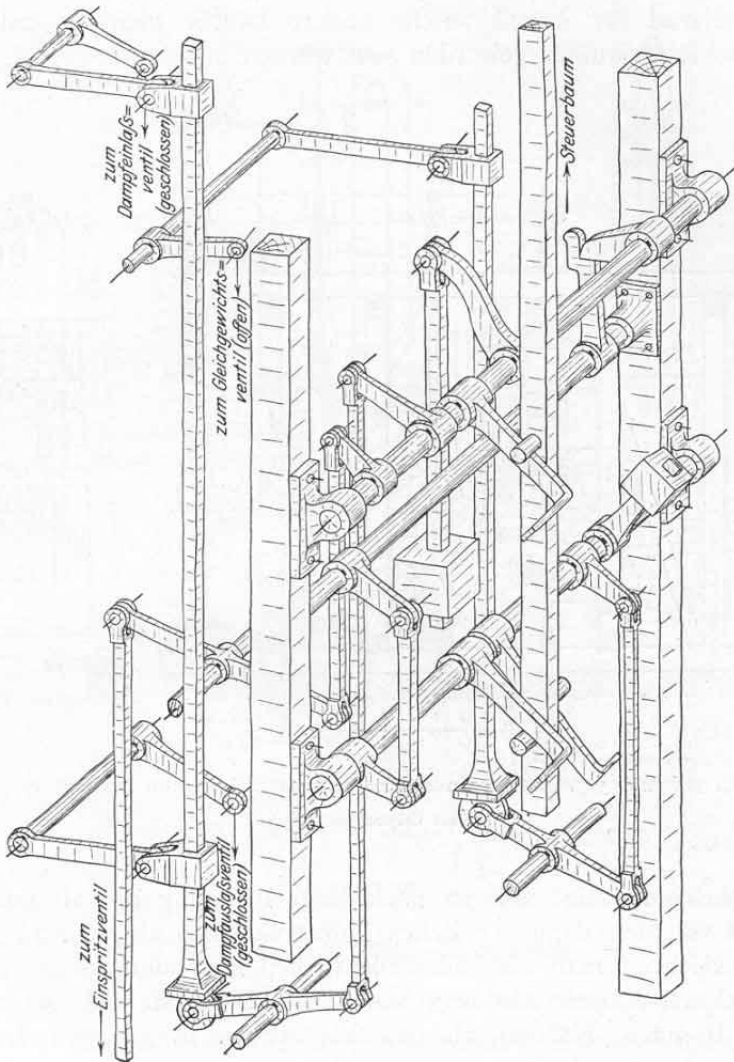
Steuerung zu einer Pumpmaschine von Dinnendahl 1806.
